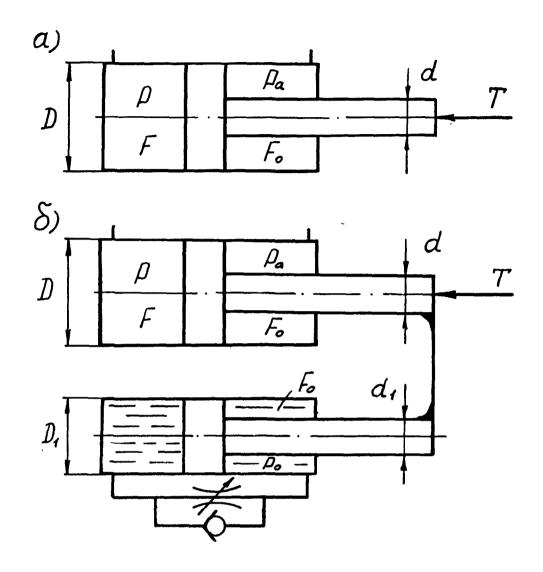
Расчетные схемы: а - пневмоцилиндра двустороннего действия; б - пневмоцилиндра с гидроцилиндром
